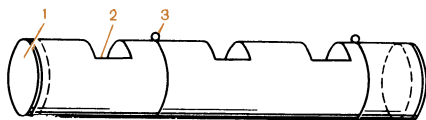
Поилка из асбестоцементной трубы: 1 — консервная банка-затлушка, 2 — окошко для питья; 3 — проволоочная скоба-крепление
